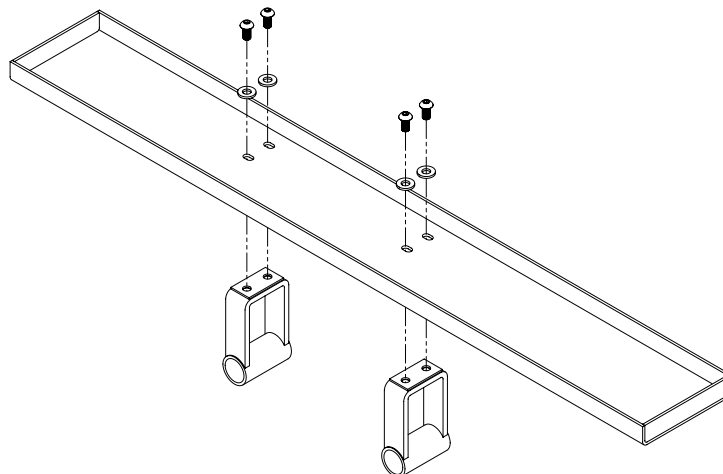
Assemblage de la plaque d'arrêt sur le rail de roue
